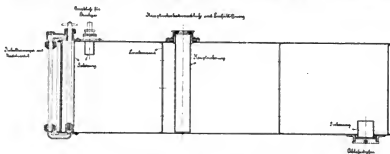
Explosions-sicherer Benzintank der „Feg“ in Salzkotten.
